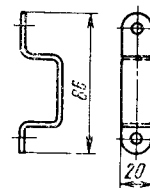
Скоба K474 для крепления шинопровода ШОС-67 на плоских основаниях (стенах, потолках, кронштейнах).
